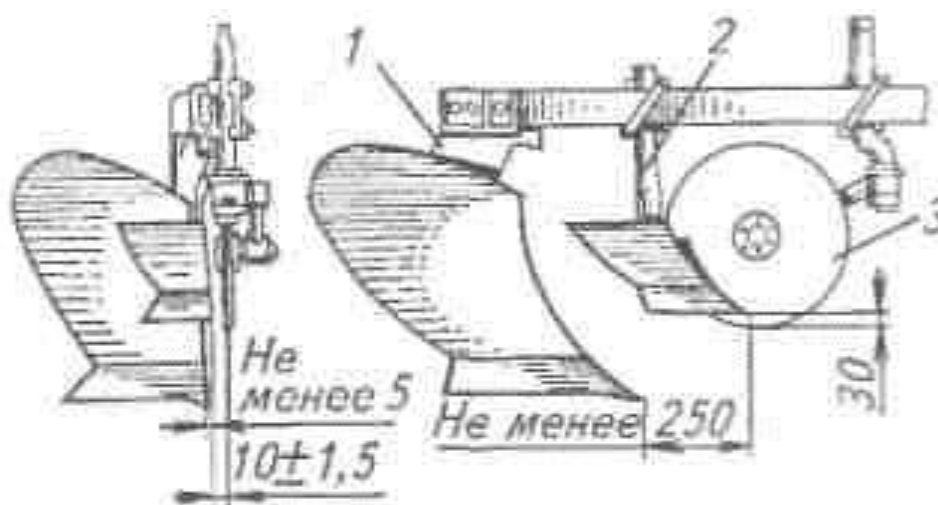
Установка дискового ножа и предплужника (размеры указаны в мм): 1 – корпус плуга; 2 – предплужник; 3 – дисковый нож
